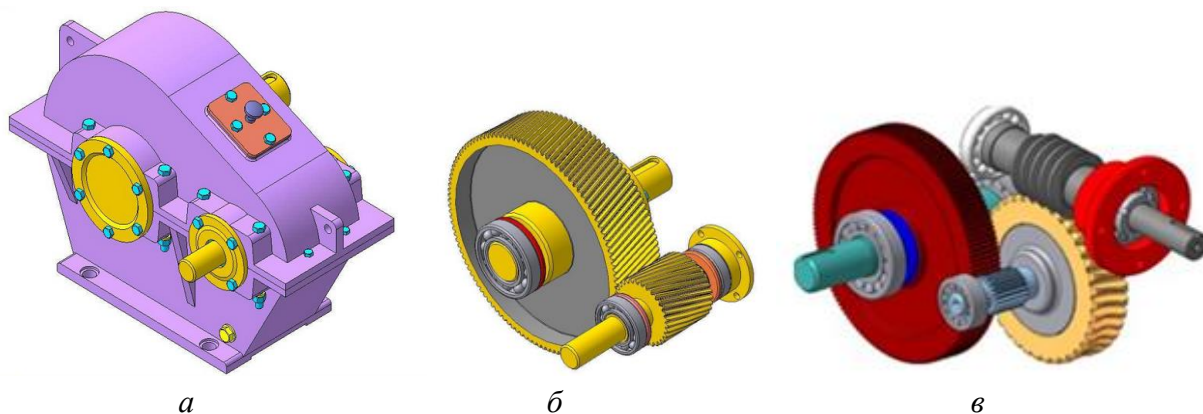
Цилиндрический зубчатый одноступенчатый редуктор – *а*; передачи зацеплением: цилиндрическая зубчатая – *б*, цилиндрическая зубчатая и червячная – *в*.
